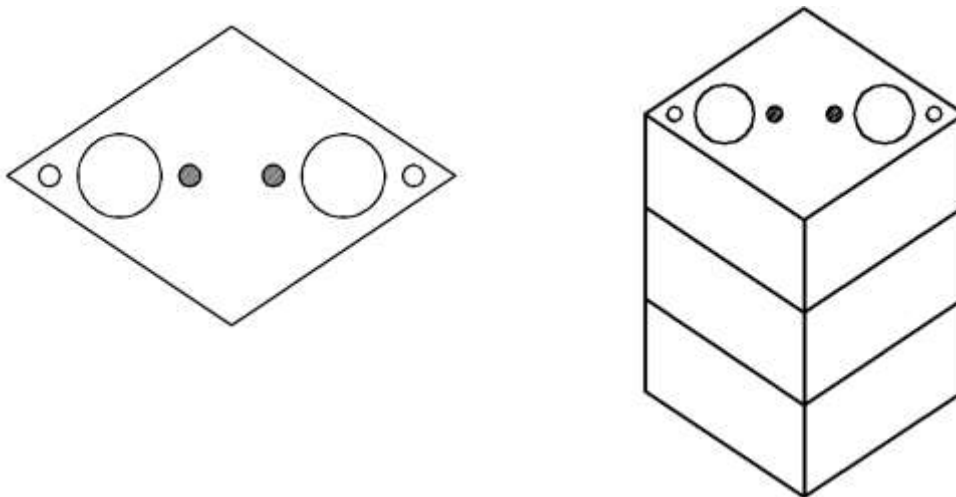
Topología de ensamblado de la pila vista en planta y en perspectiva
